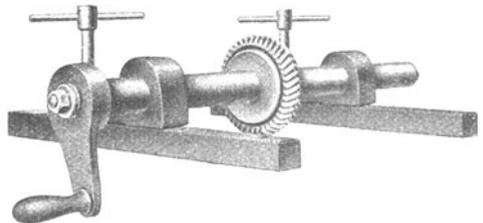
Abrichtapparat für Sandsteine mit Fräser.
